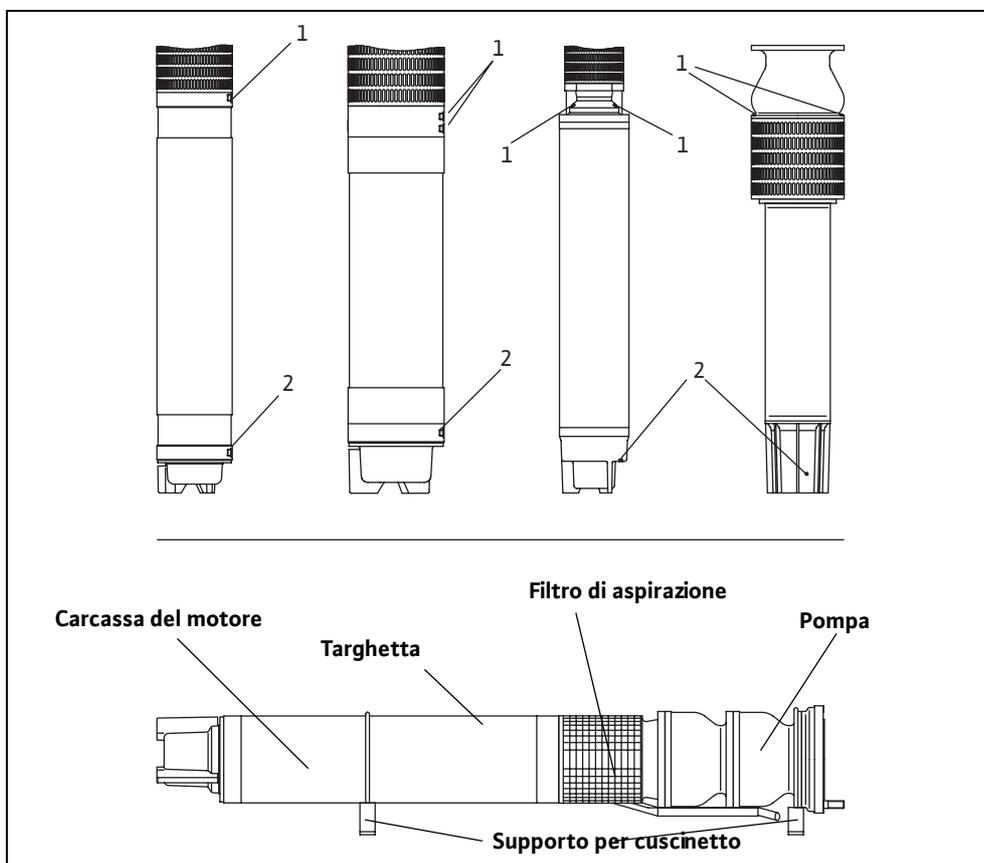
Controllo e riempimento della carica del motore - montaggio verticale e orizzontale
